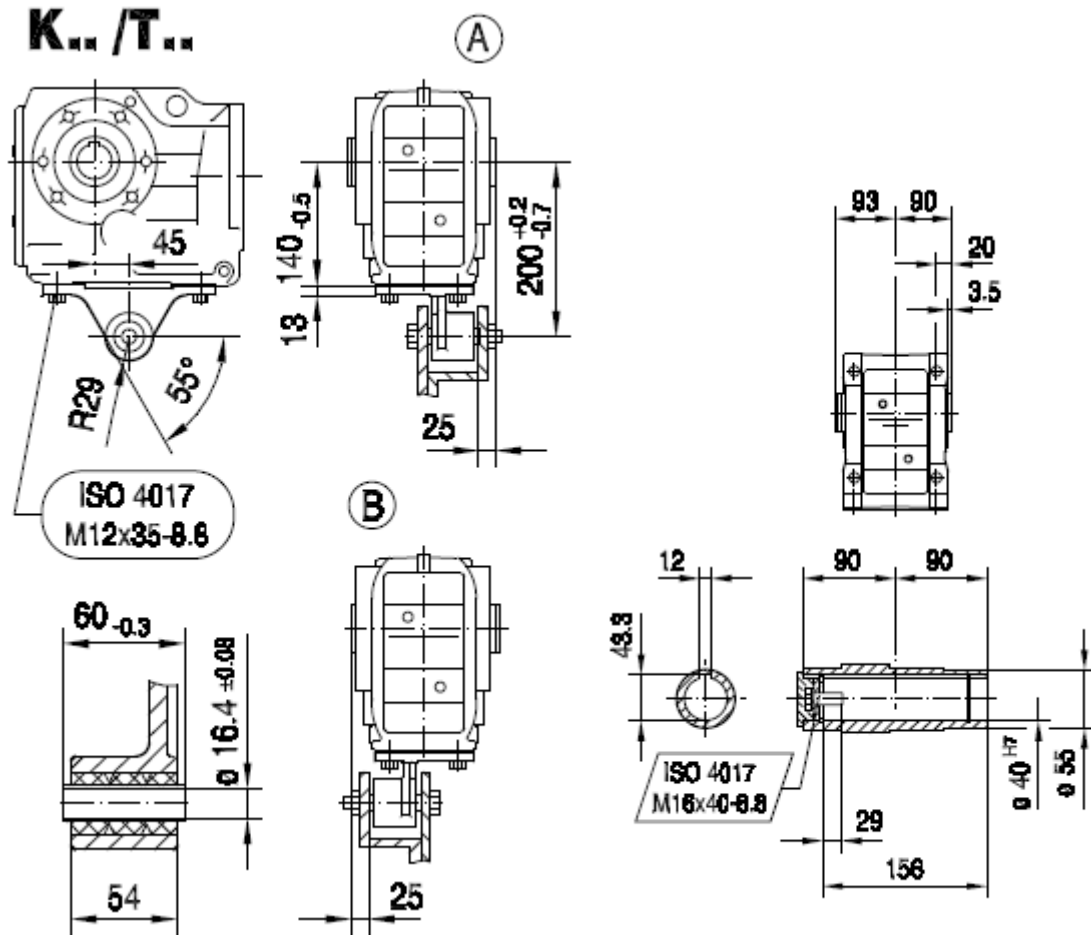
Principales dimensiones del reductor SEW mod KA67/TA
